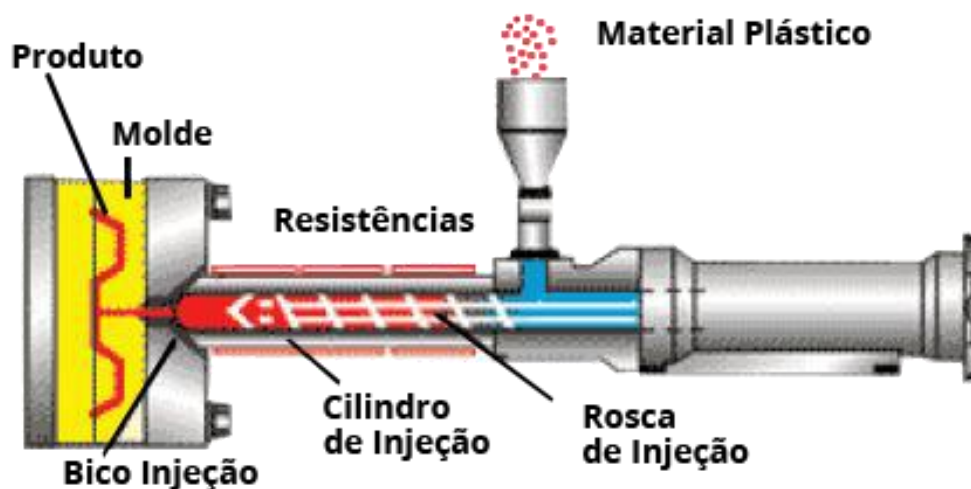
Demonstrativo do Processo de Moldagem por injeção
